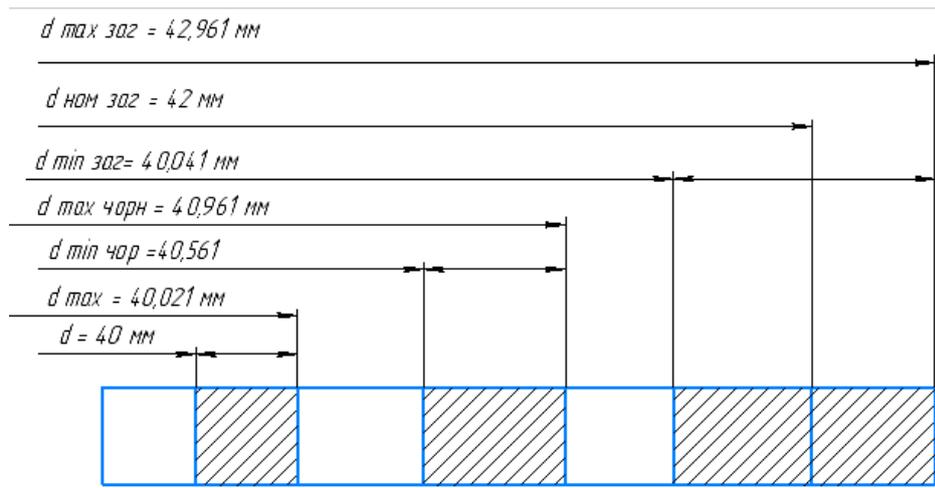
Схема розташування допусків та припусків
